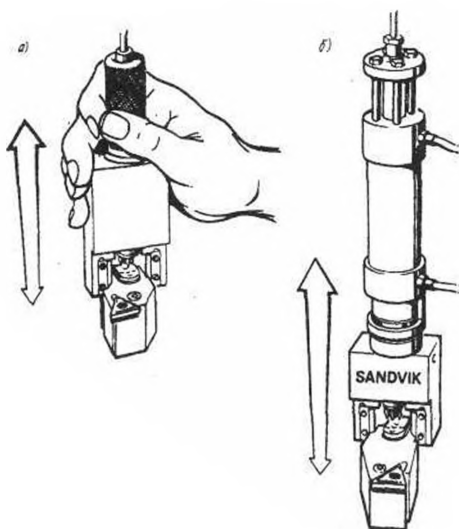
Способи установки адаптера на інструментальний блок:
